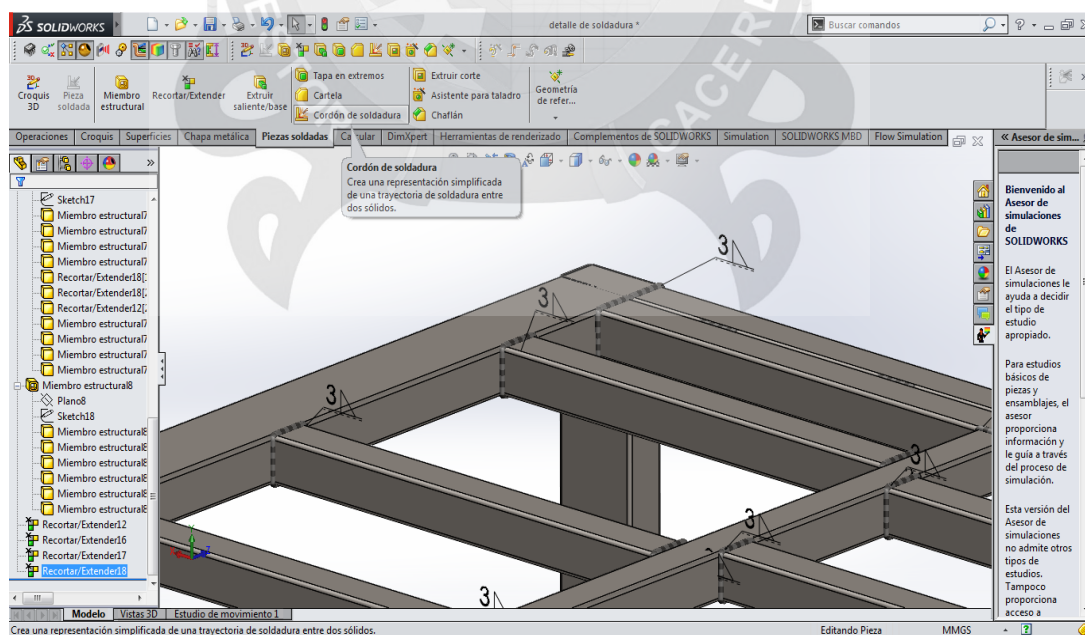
Diseño en SolidWork, asignación del cordón de soldadura
